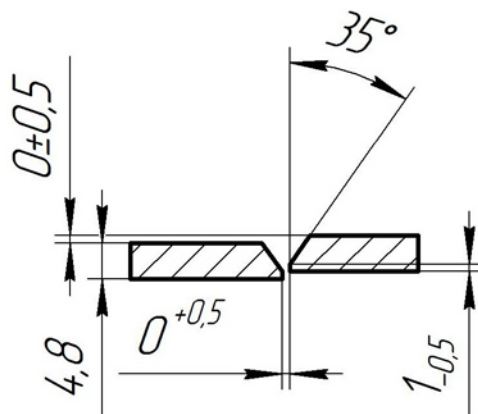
Эскиз кромок обечайки подготовленных под прихватку
